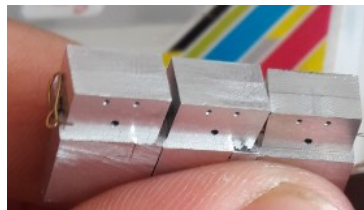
Resultado del proceso de manufactura mediante CNC [22].
